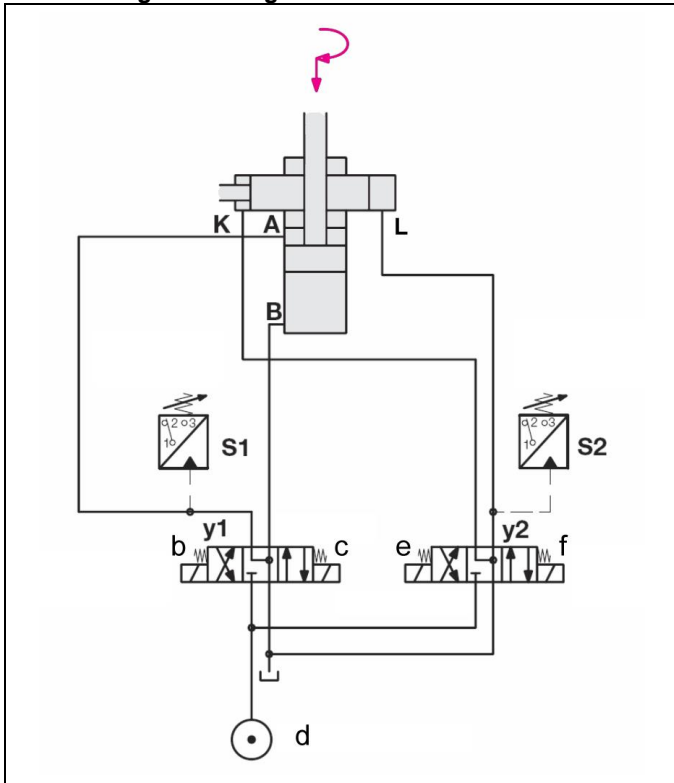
Hydraulikplan, Steuerung durch Druckschalter
